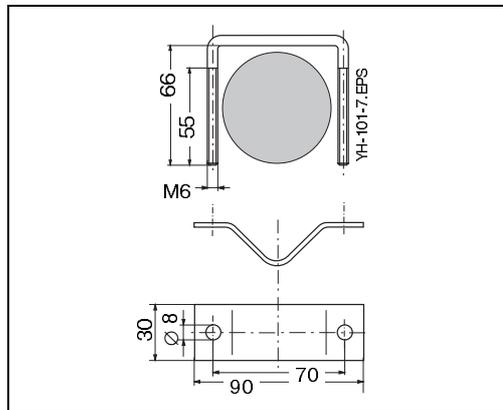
Комплект крепежных элементов для установки на круглой опоре козырька-навеса СУУ 101, если монтаж производится не на арматурном держателе СУН 101
